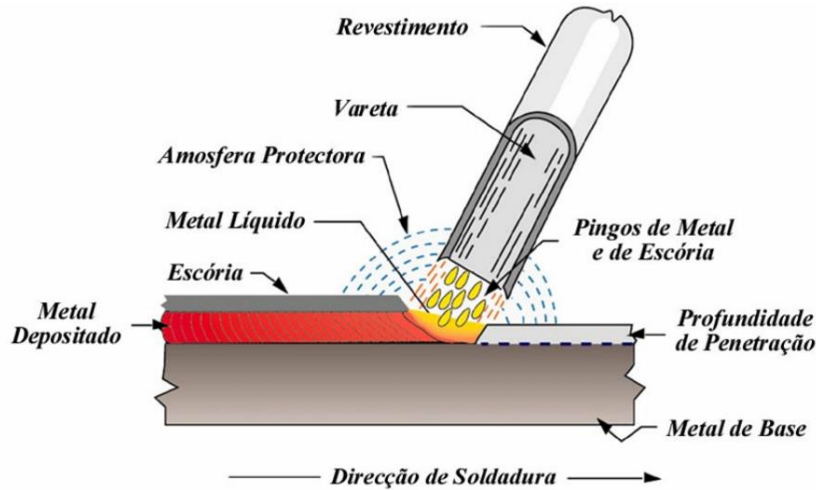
Representação esquemática do processo de soldadura por elétrodo revestido (fonte: ISQ).
